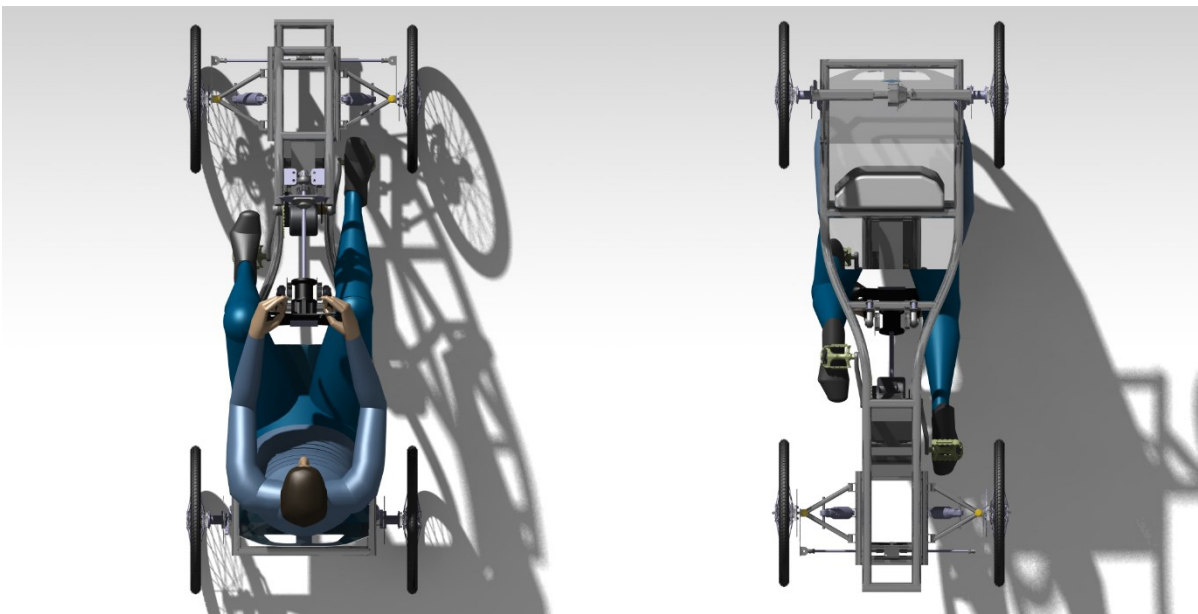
Vista superior e inferior da estrutura do E-Pedal. Fonte: Elaborado pelo autor.
